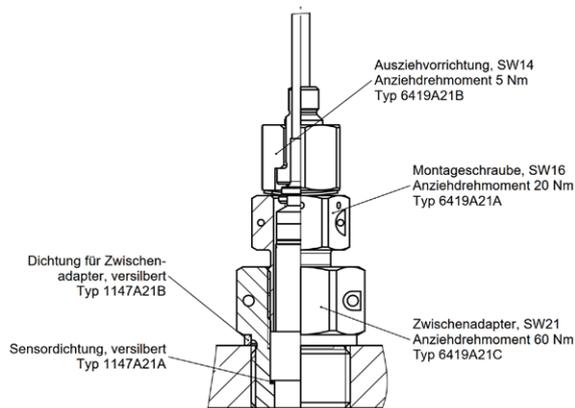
Montage mit Zwischenadapter Typ 6419A21C, Montageschraube Typ 6419A21A, Ausziehvorrichtung Typ 6419A21B sowie Dichtung Typ 1147A21A und Typ 1147A21B
